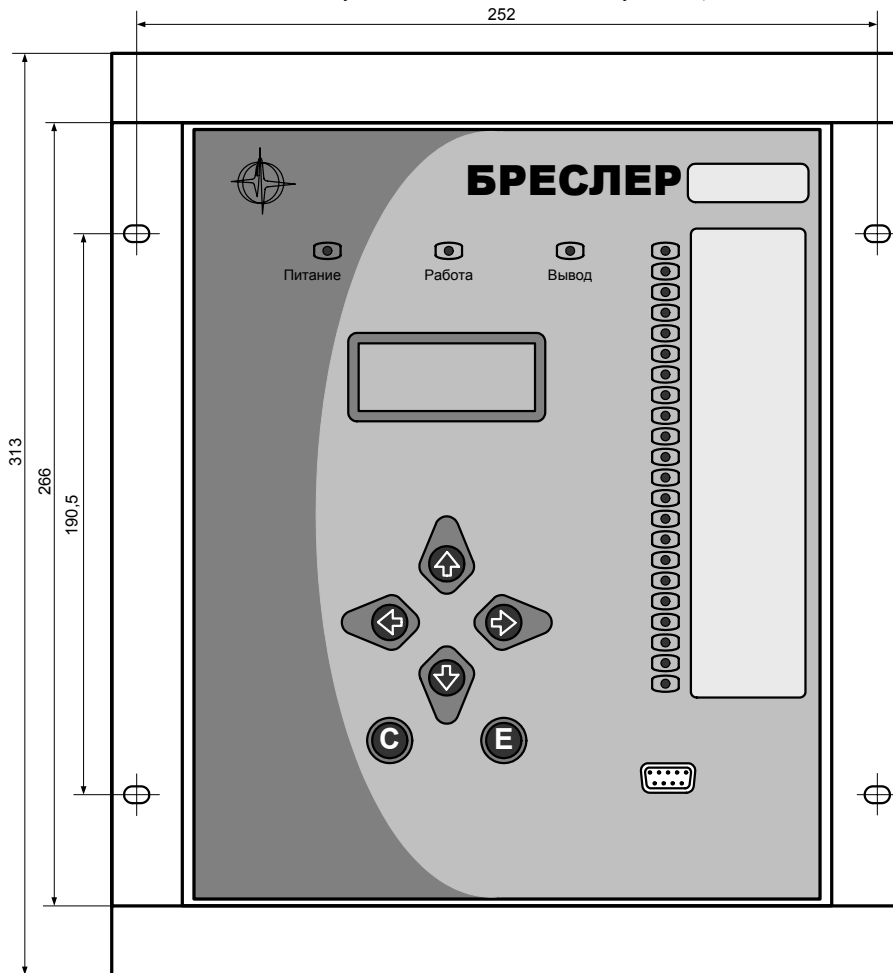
Внешний вид, габаритные и установочные размеры терминала
